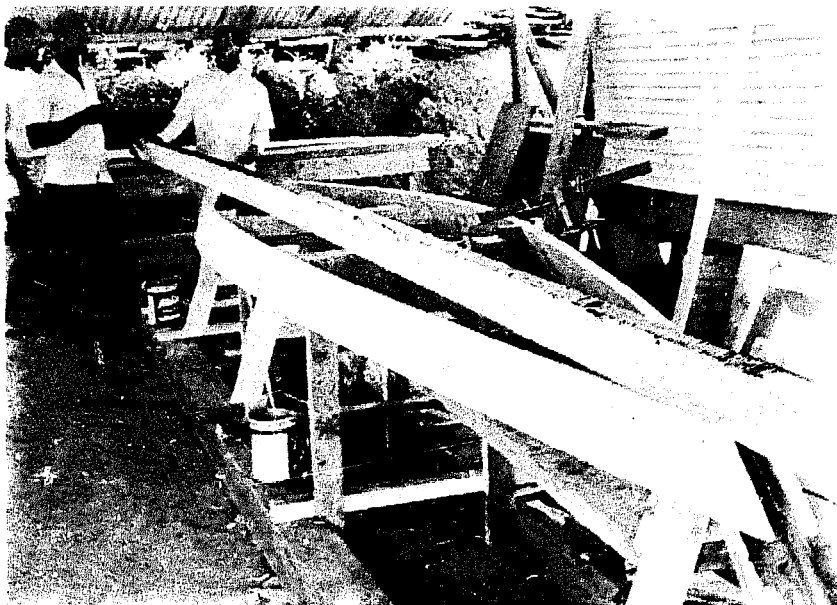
Appliquer le produit d'étanchéité sur une rive de la planche
